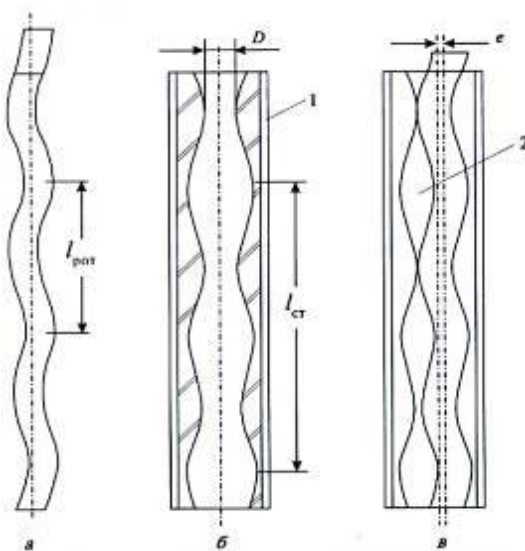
Глубинный винтовой насос: а - ротор; б - статор; в - насос в сборе; 1 - корпус насоса; 2 - полость между статором и ротором.
